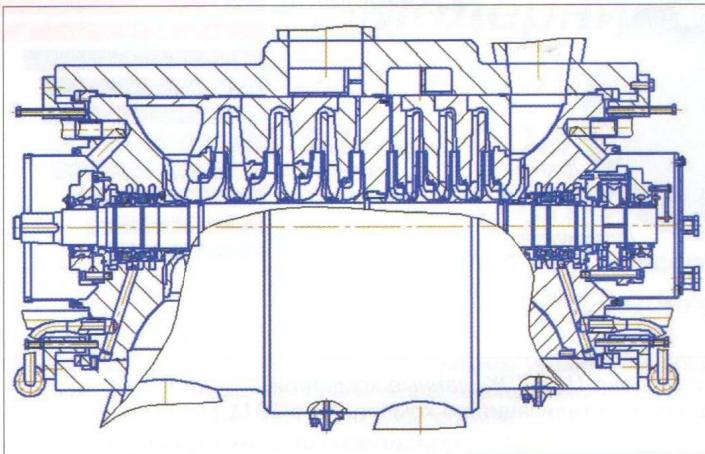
Разрез корпуса компрессора 4ГЦ2-184/13,5-76
